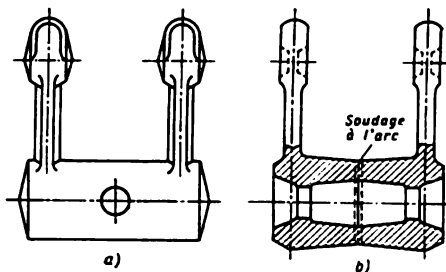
Construction d'un même élément de machine: (a) entièrement estampé; (b) soudé
